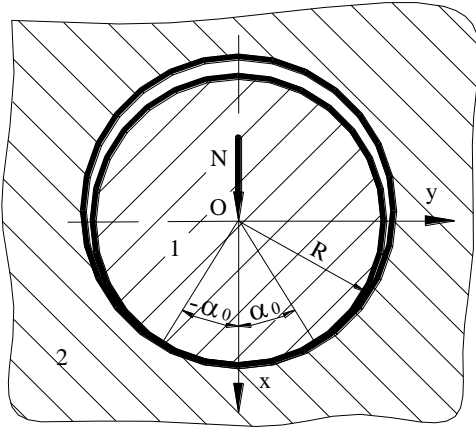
Розрахункова схема трибосистеми циліндричного спряження: 1 – головка прутка; 2 – ланка з'єднання.
